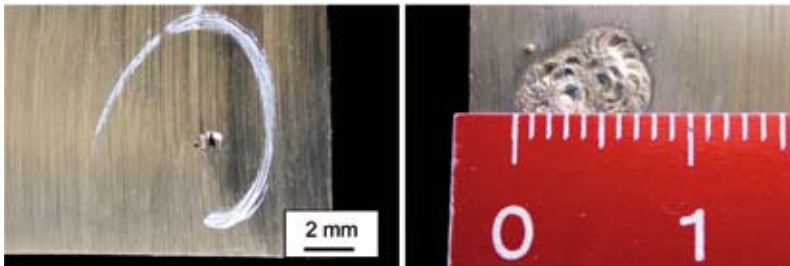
Pore an der Oberfläche vor (links) und nach dem manuell geführten Laserstrahlschweißen (rechts)
